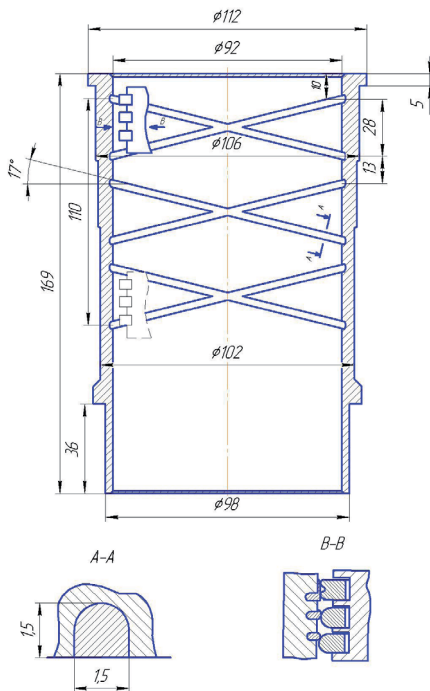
Общий вид гильзы цилиндров двигателя УМЗ-417 с изменёнными физико-механическими свойствами
